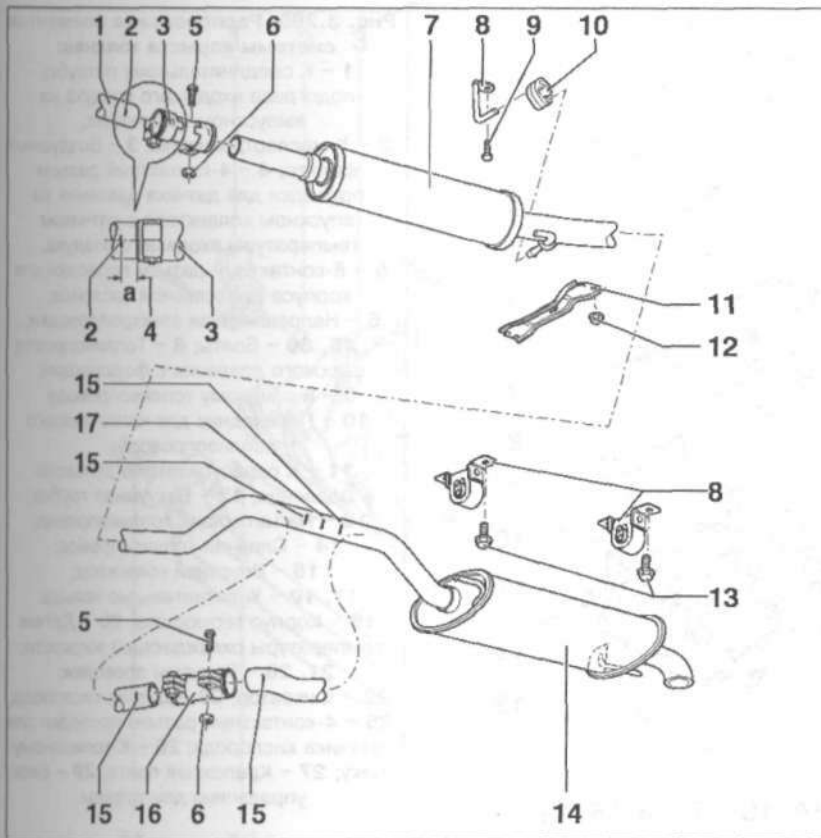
в. Глушитель с опорами автомобилей Caddy:
